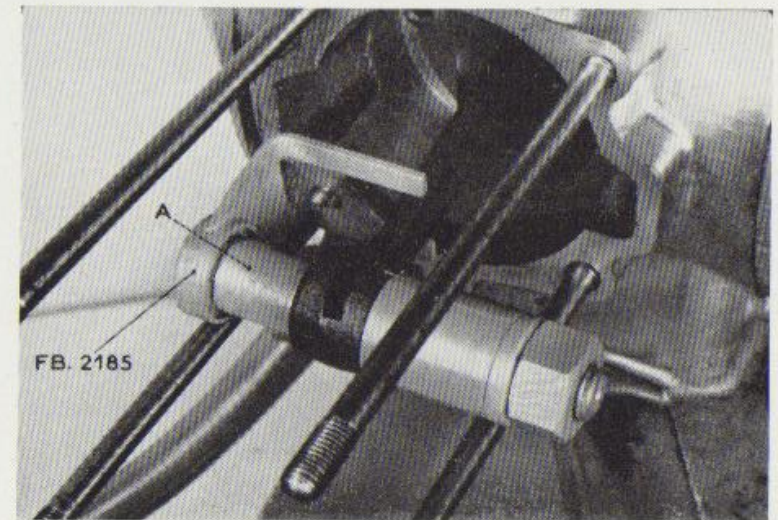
Outil pour le montage et démontage de la bague de pied de bielle (FB.2185).
